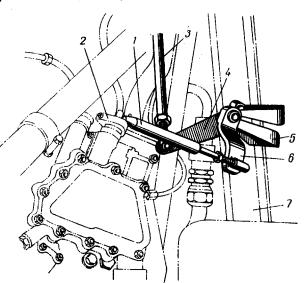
Элементы управления форсажной камерой на рычаге управления двигателем.
